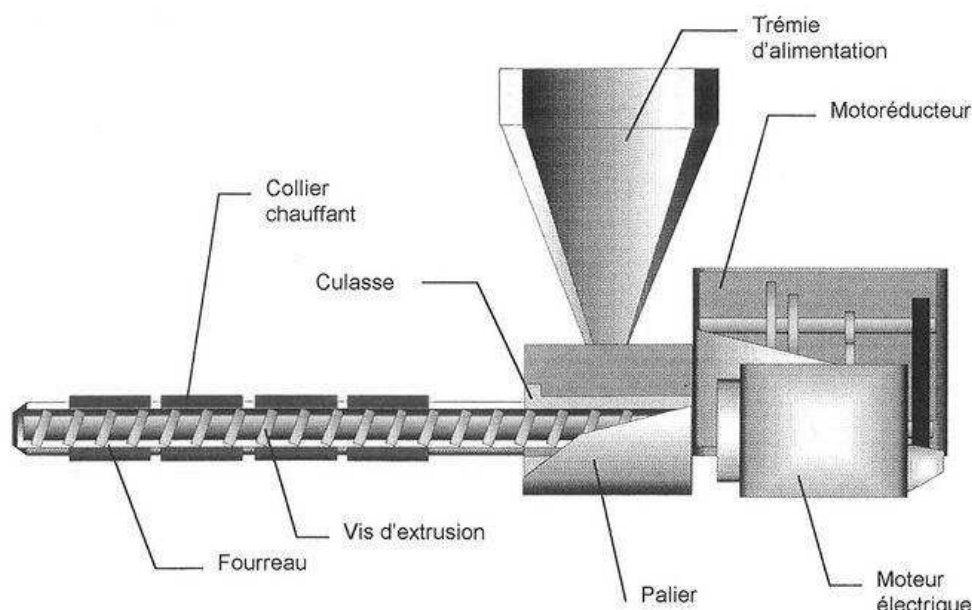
Schéma d'une machine d'extrusion de type monovis
